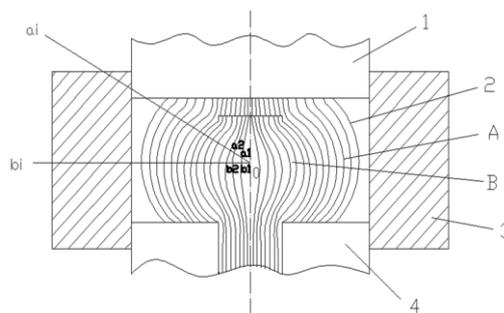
Схема течения металла при деформировании сборной заготовки: 1 – пуансон; 2 – сборная заготовка; 3 – матрица; 4 – выталкиватель; А – головная заготовка; В – стержневая заготовка
